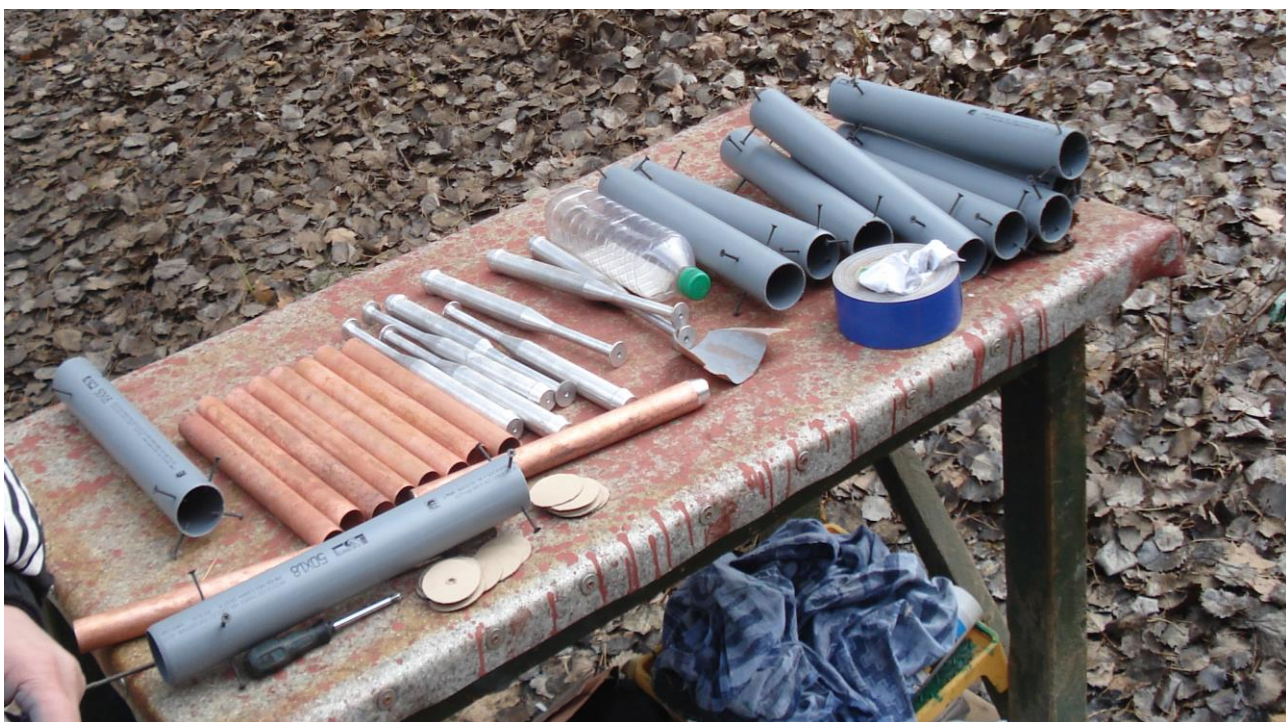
Заготовки для виготовлення дослідно-промислової партії
